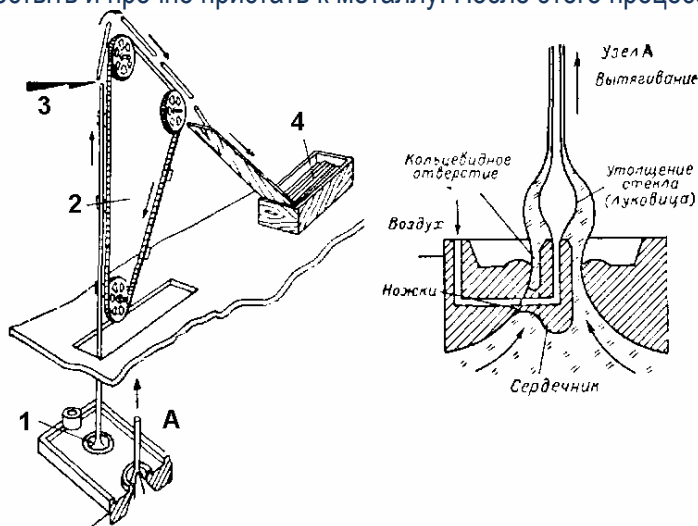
Установка для вытягивания трубок при помощи лодочки: 1 — лодочка; 2—вытягивающее устройство; 3—отрезание трубок в размер; 4—готовые трубки
